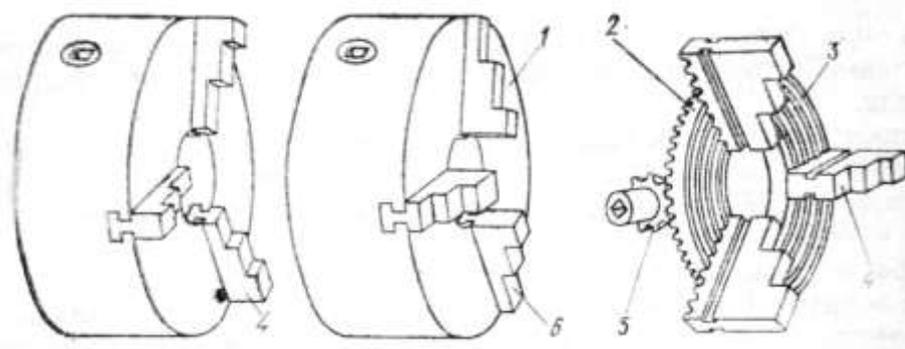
Конструкція трикулачкового самоцентруючого патрона
